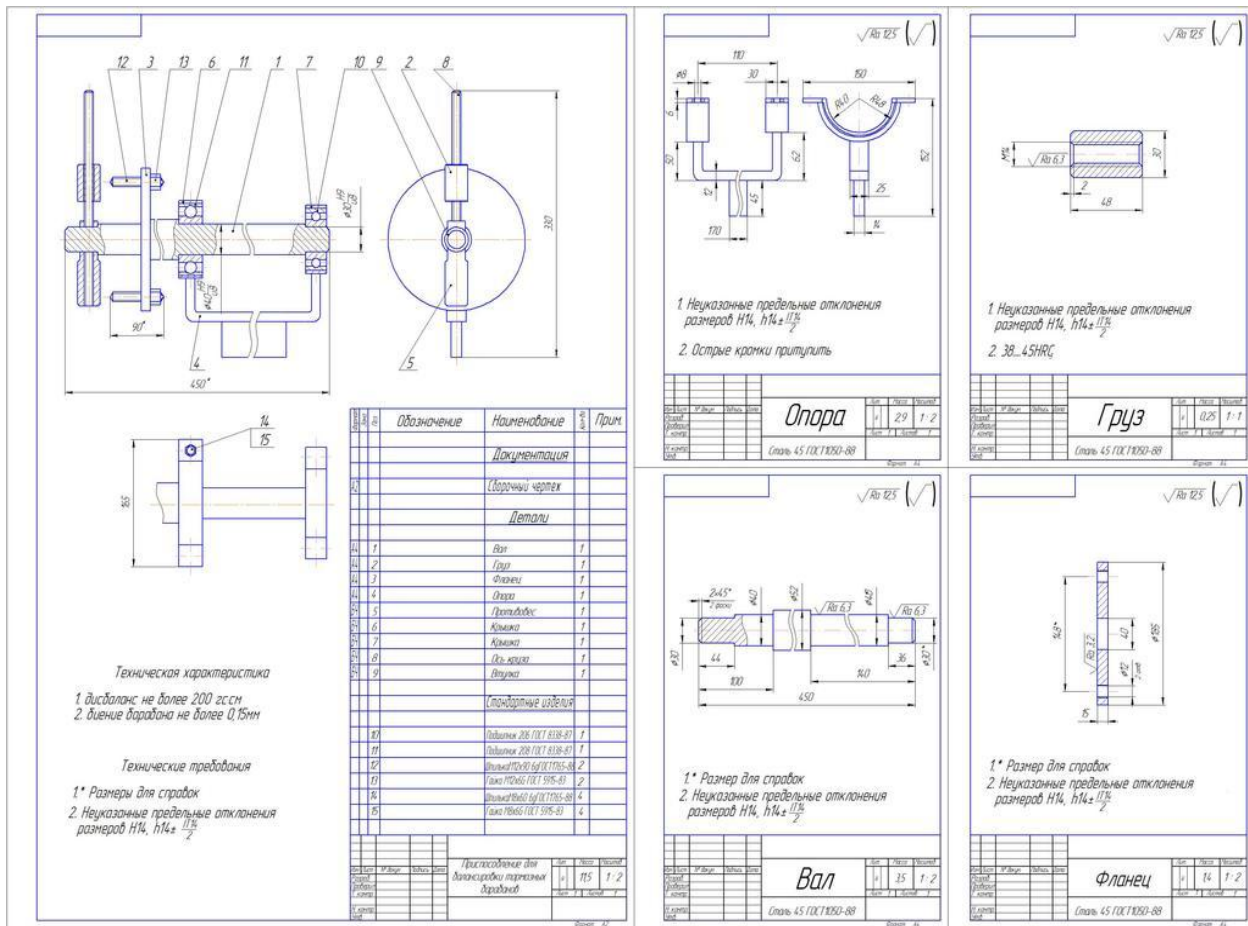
Сборочный чертеж и рабочие чертежи приспособления
